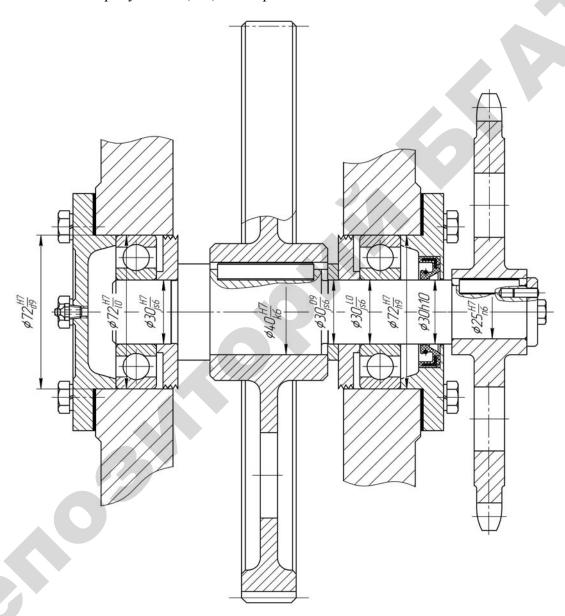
Фрагмент сборочного чертежа одноступенчатого редуктора с цилиндрической передачей
